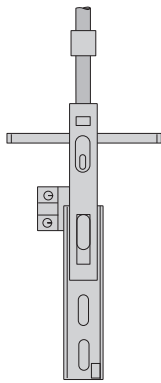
L-Antrieb für Beton- bzw. Stahlmast
